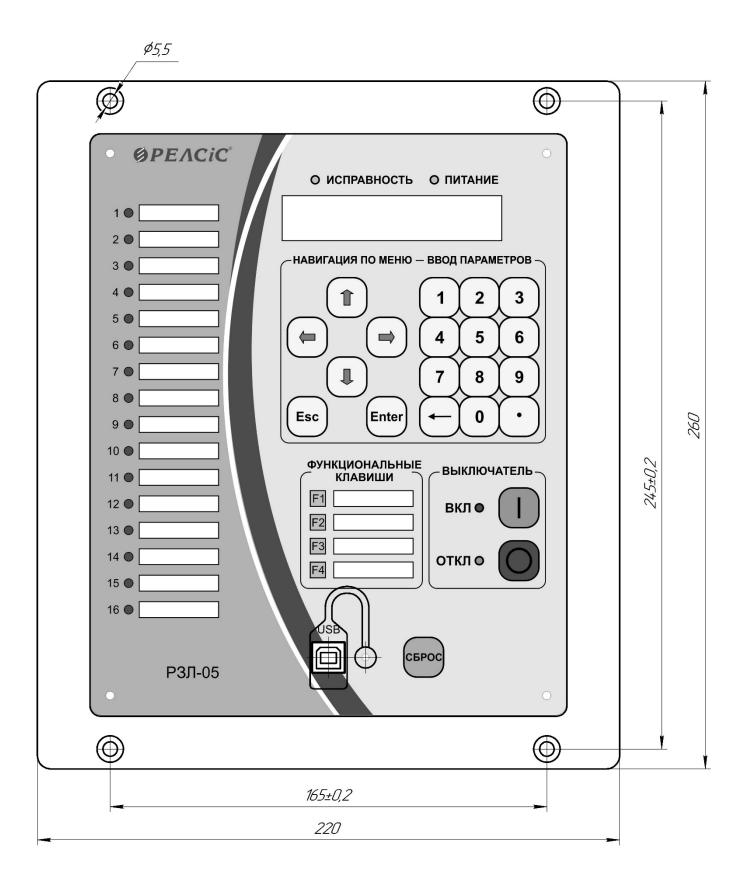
Габаритные и установочный размеры, внешний вид передней панели устройств Р3Л-05.Ф5, Р3Л-05.Ф6
